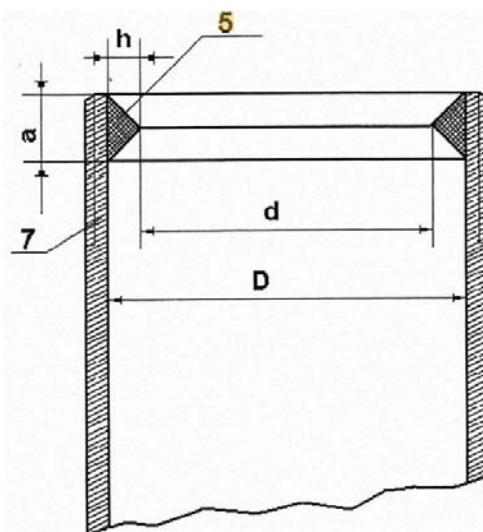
Диспергатор в виде кольца с конусообразной поверхностью [22] (5 – диспергаторное кольцо; 7 – торец ОЛК; a – ширина кольца; h – высота конуса кольца; D, d – внутренний и внешний диаметры кольца соответственно)
